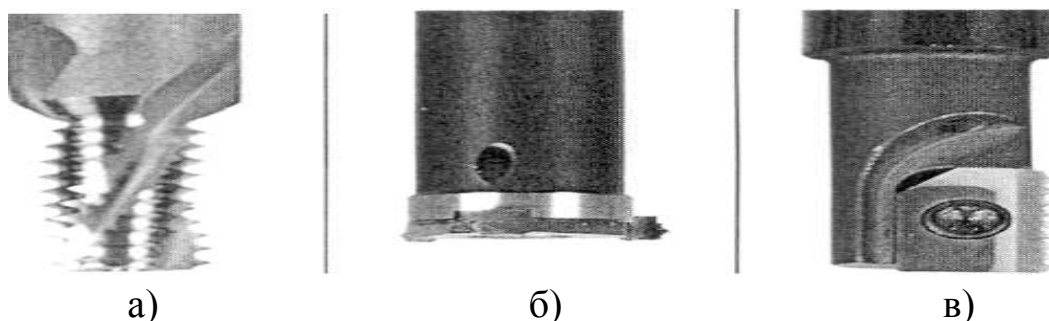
Инструменты для нарезания внутренней резьбы: а – метчик, Q355=0; б – резбовой резец, Q355=1; в – резбовая гребенка, Q355 > 1
